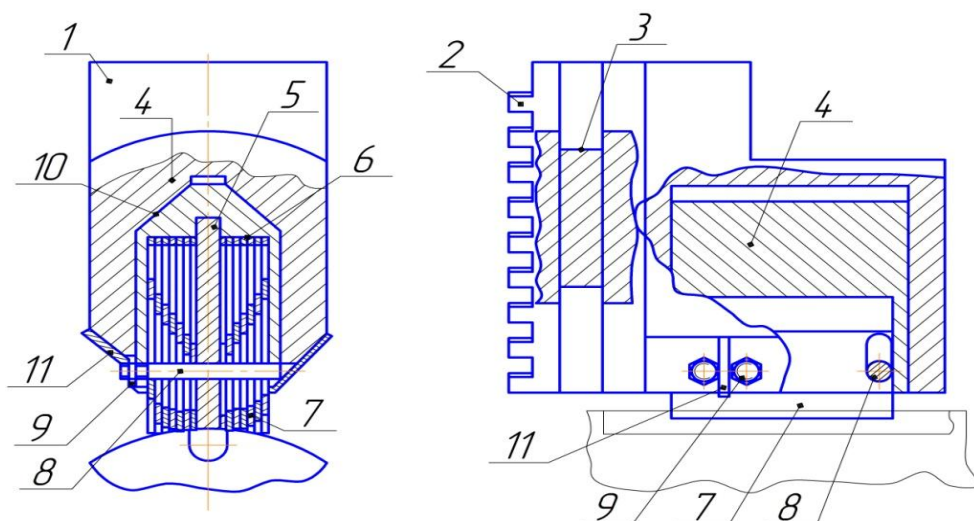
Кулачок токарного патрона із змінною рамкою підпружинених пластин.
